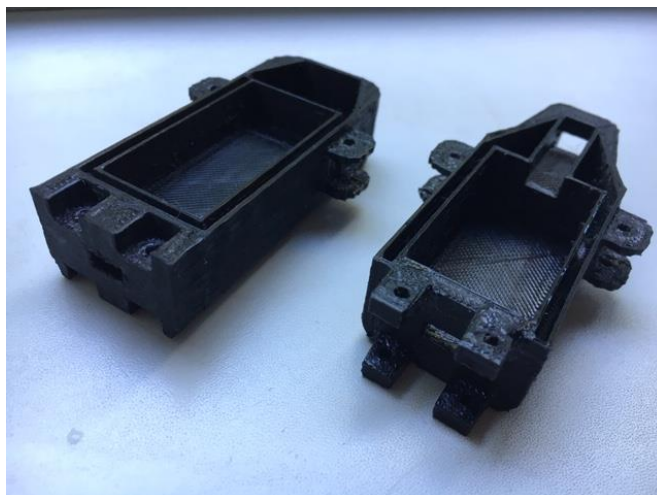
Прототип модели корпуса, полученный с помощью 3d печати
